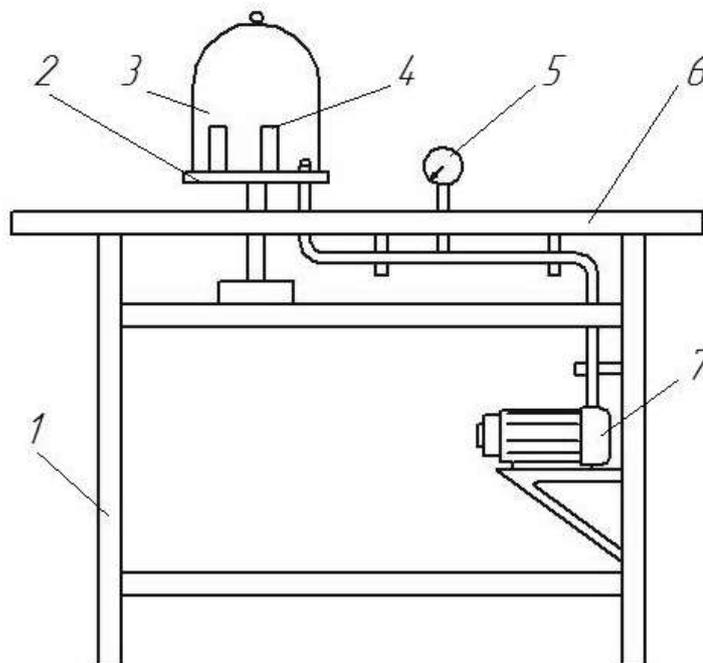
Схема вибровакuumной обработки опок с формовочной суспензией
